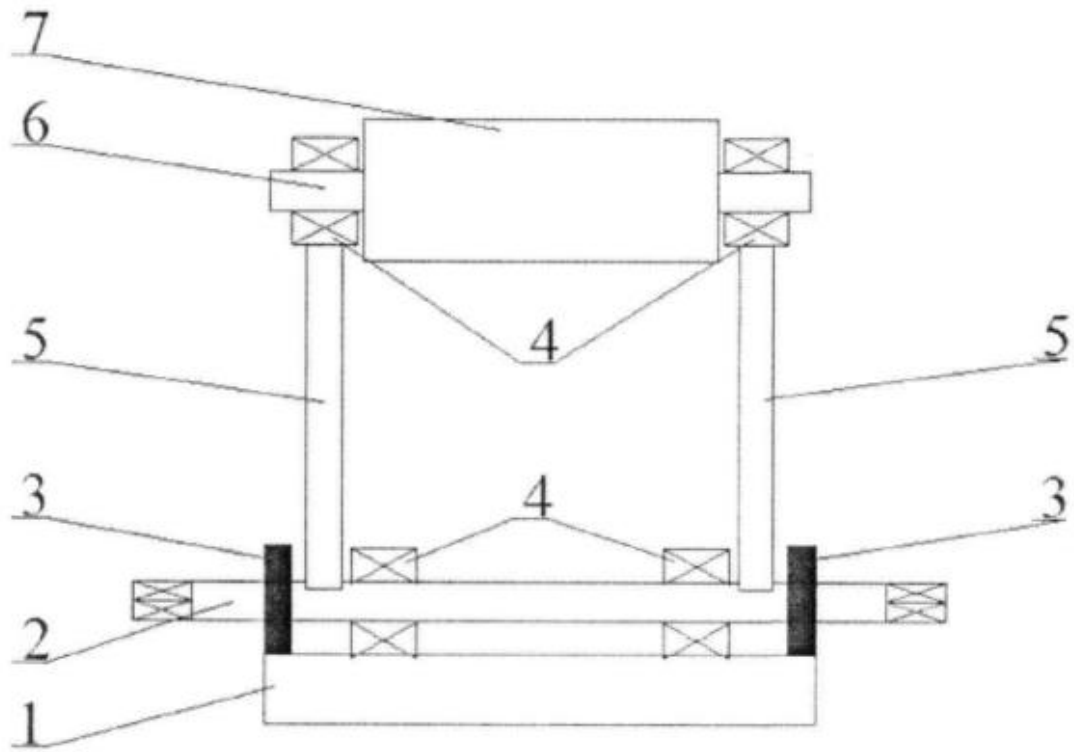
Роликовий вузол стрічкового транспортера: 1 - рама; 2 - пучковий торсіонний вал; 3 - храповий механізм; 4 - обойми з кульковими підшипниками; 5 - важелі; 6 - 60 вал натяжного барабана; 7 - натяжний барабан [3].
